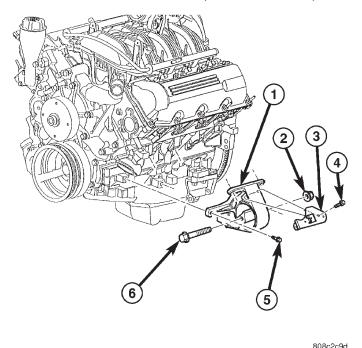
Soporte del aislador del motor 3.7L izquierdo
